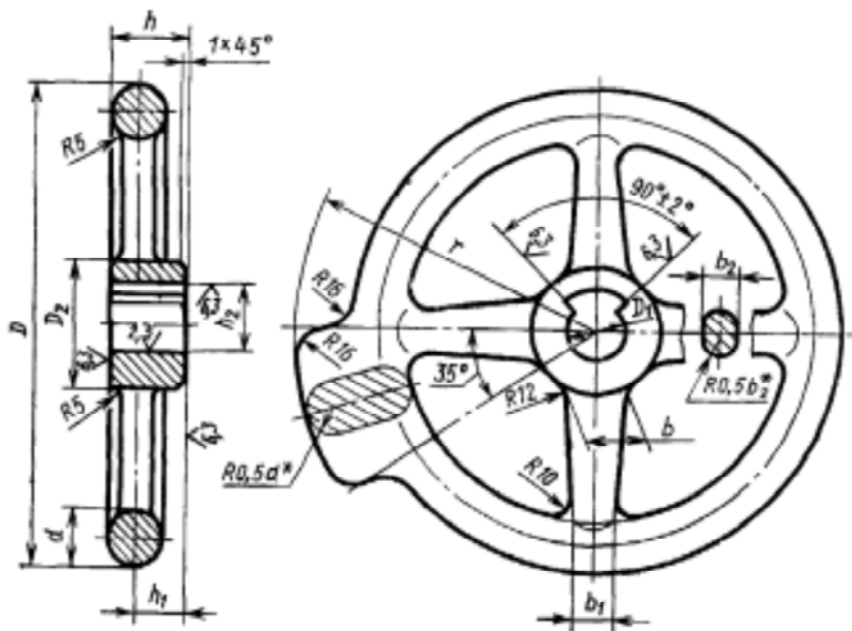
Конструкция и размеры маховика приспособления для удаления стержней
